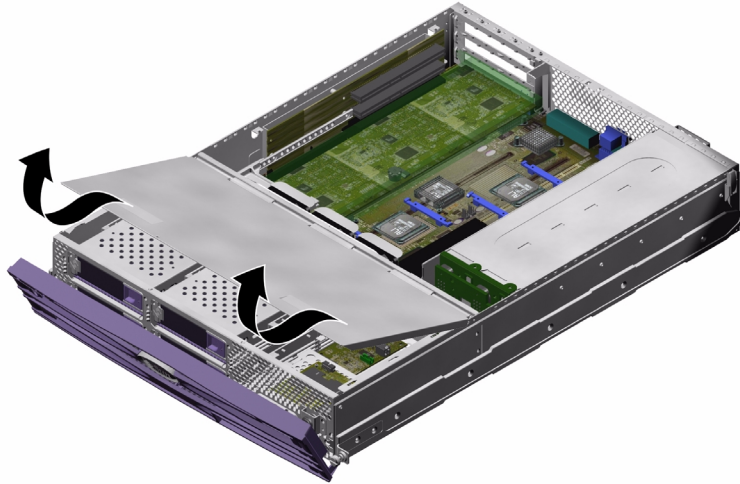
Extracción de la sección frontal de la cubierta
